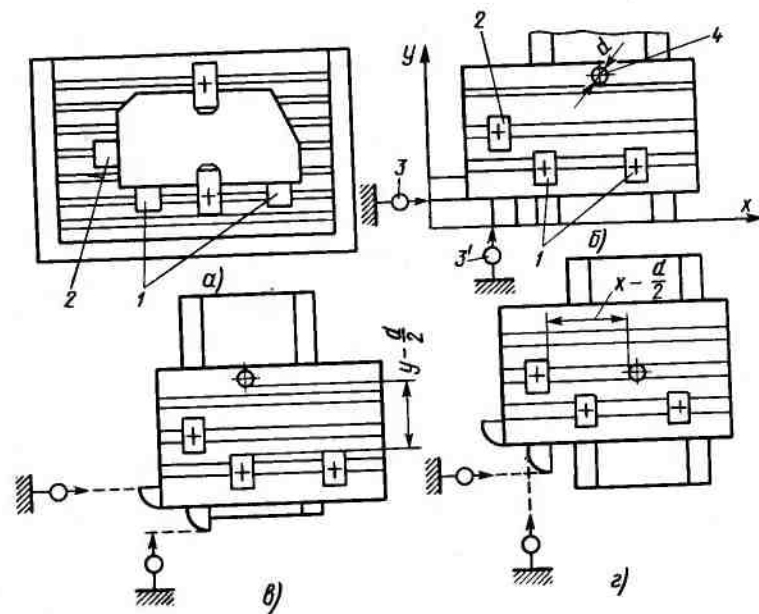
Схема базирования заготовки на столе фрезерного станка с ЧПУ:
